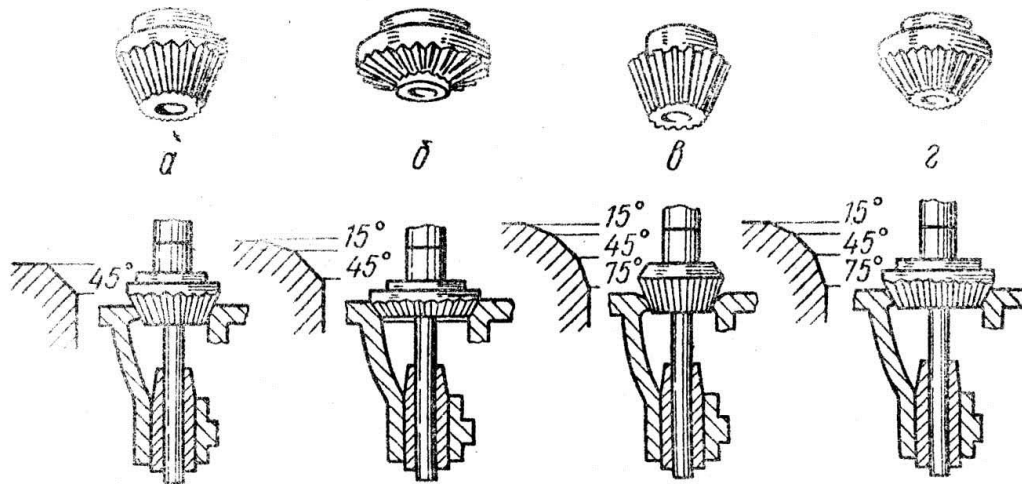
Обробка клапанного гнізда фрезами. Фрезерування під кутом:
